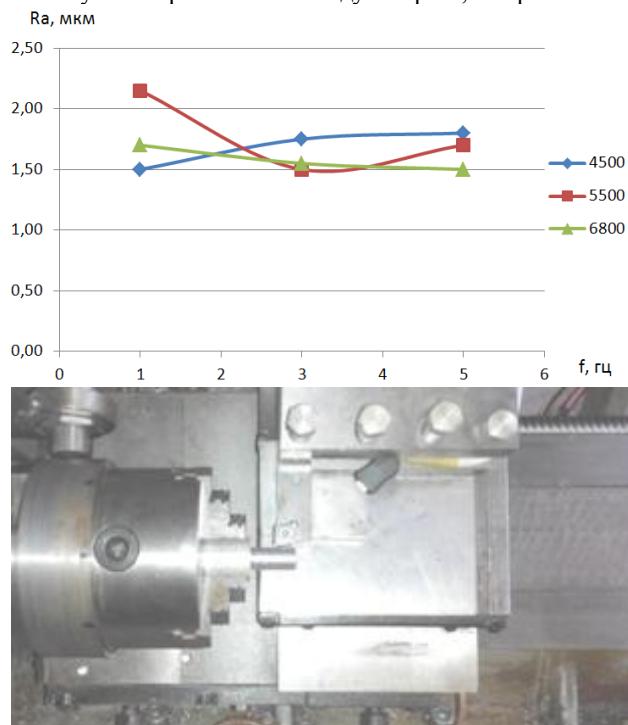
Вплив модуляції частоти обертання заготовки на якість обробки
